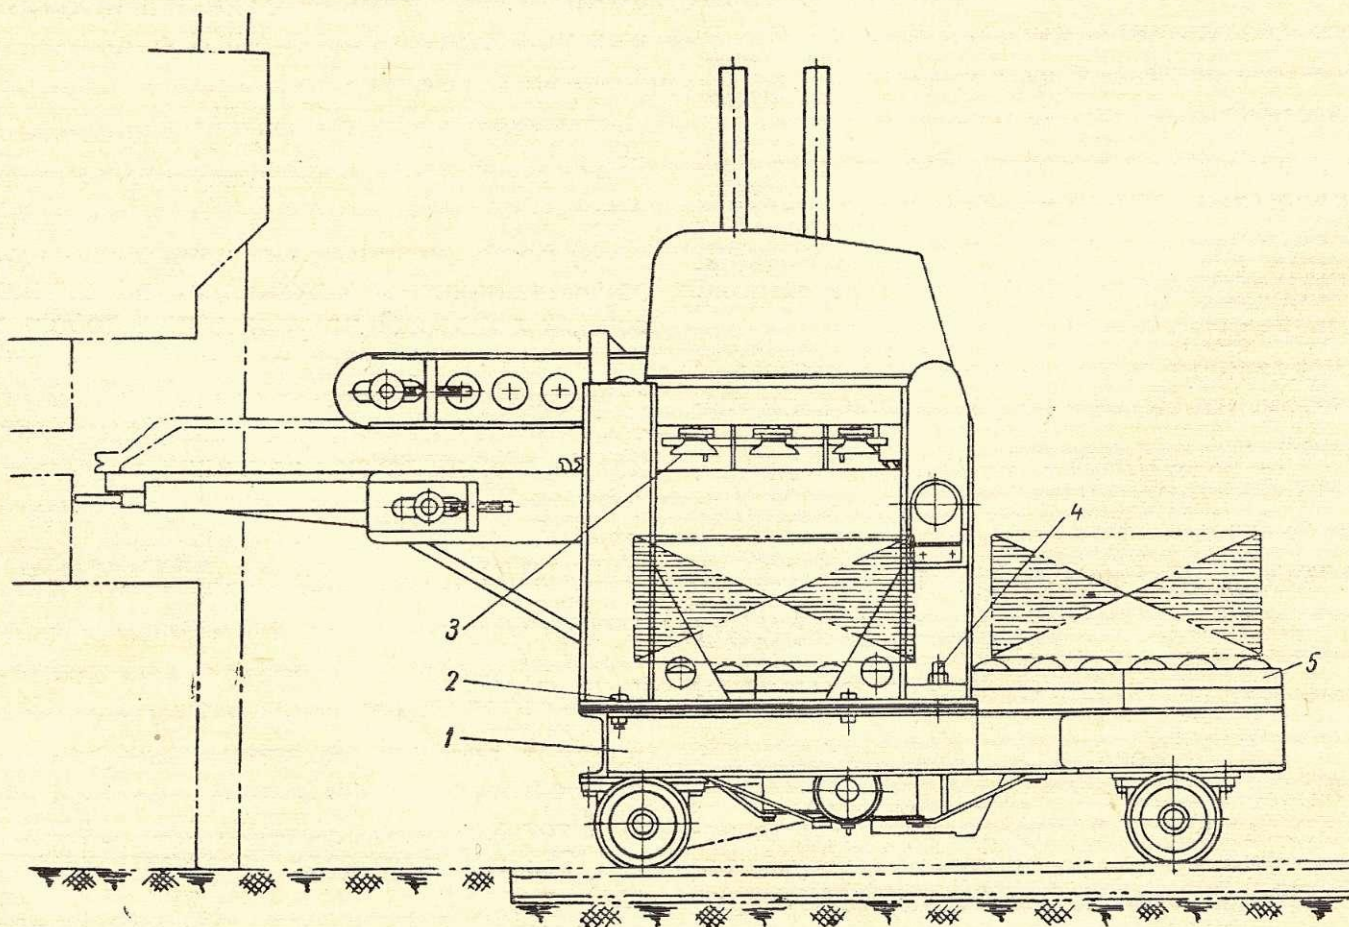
Механизм поштучной подачи крупногабаритного материала в штамп прессы.
